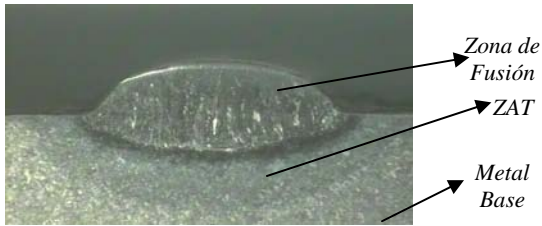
Depósito de soldadura en acero CA6NM.
